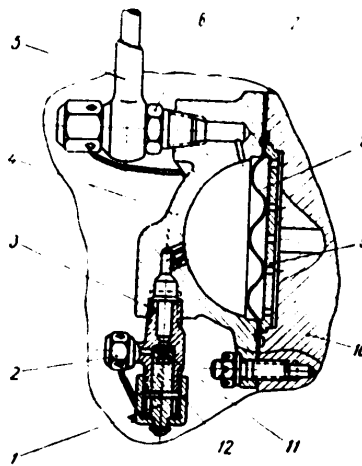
а. Жиклер переменного сечения. 1—игла; 2—втулка (жиклер); 3—переходная втулка; 4—обратный клапан; 5—колпачок; 6—пружина; 7—корпус обратного клапана; 8—прокладка; 9—шайба; 10—прокладка; 11—накидная гайка; 12—замок иглы.
